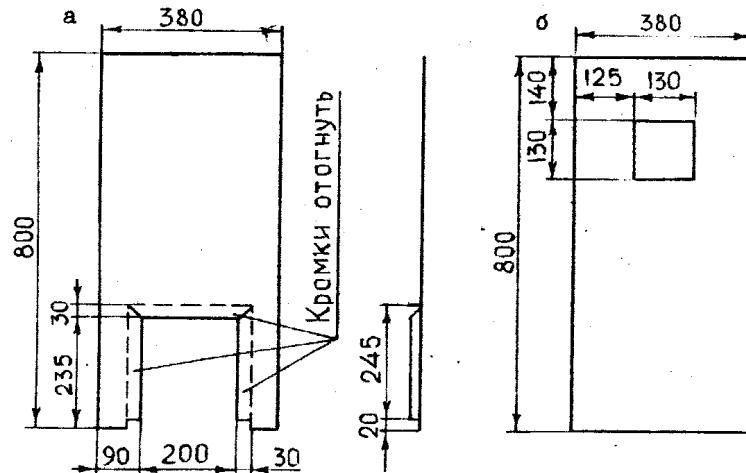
а – Верхний фасадный облицовочный лист с отверстием для варочной камеры. б – верхний задний облицовочный лист
